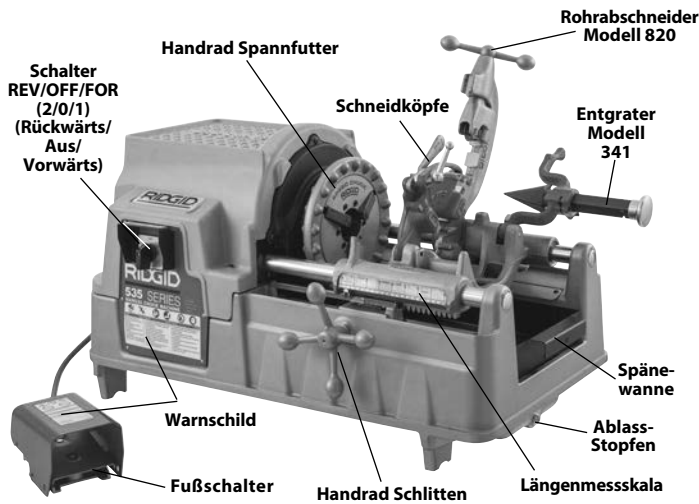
A – Gewindeschneidmaschine 535 mit Handspannfutter
